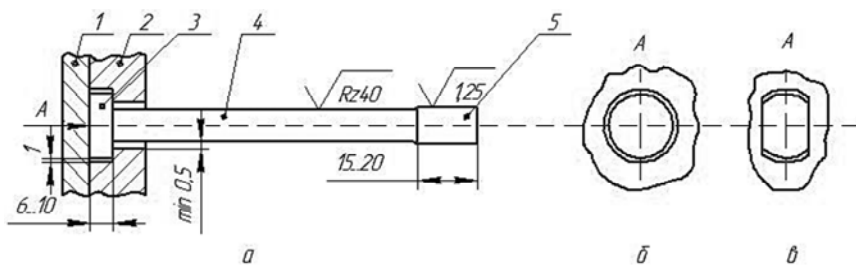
Пример крепления штифтового выталкивателя для механизированных кокилей
